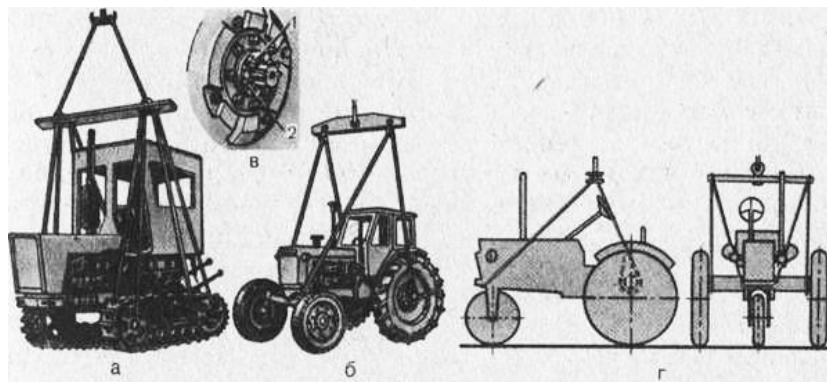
Приемы строповки тракторов: а - гусеничного; б и г - колесного; в - устройство для крепления; 1 - рым-болт; 2 - отверстие
